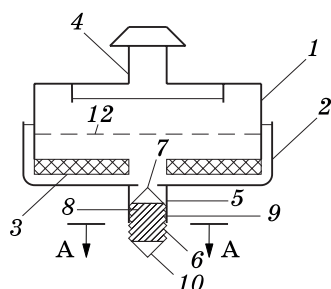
Капельница с винтовым регулятором подачи воды (патент 2409024): 1 – верхняя часть корпуса; 2 – нижняя часть корпуса; 3 – резиновая прокладка; 4 – входной патрубок; 5 – выходной патрубок; 6 – регулятор подачи капель; 7 – верхней конической часть; 8 – средняя резьбовая часть; 9 – каналы для прохождения через них воды; 10 – конический элемент; 11 – вогнутая образующая; 12 – сетчатый фильтр
